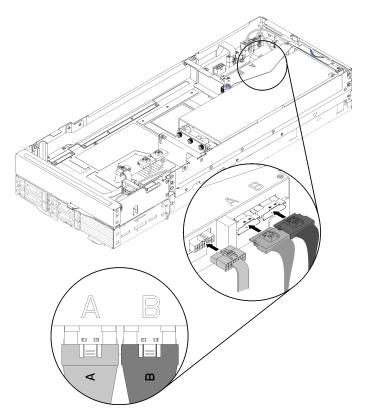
Conectando PCIe#1-A, PCIe#2-B e o cabo diverso da placa riser ao conjunto da placa riser traseiro.
